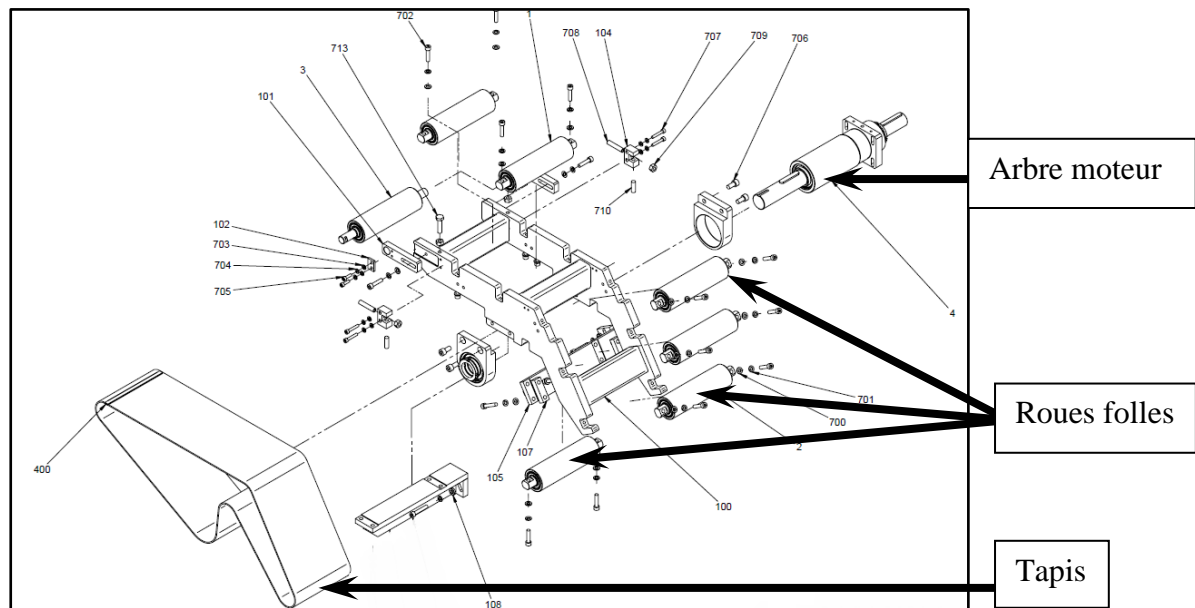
Vue éclatée d'un des convoyeurs du Final Forming
